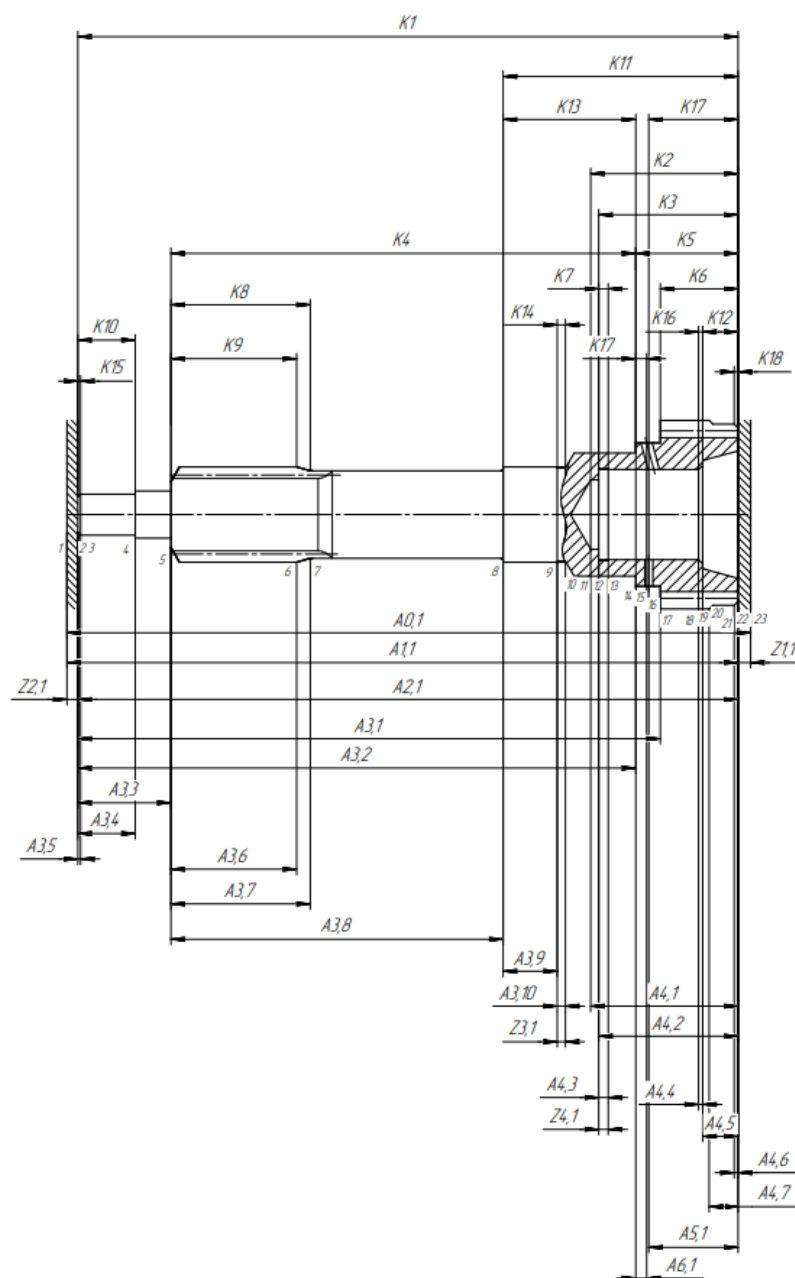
Размерная схема технологического процесса изготовления «ведущий вал коробки передач»
